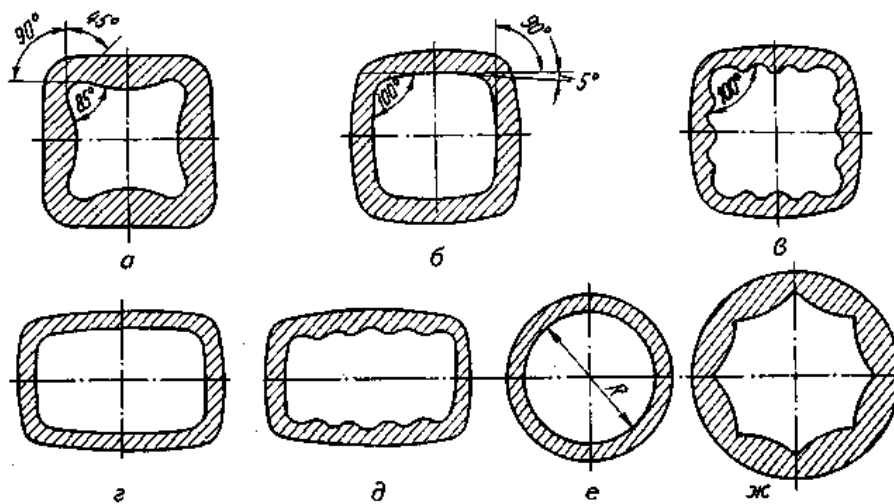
Форми (а–ж) поперечного перетину виливниць
